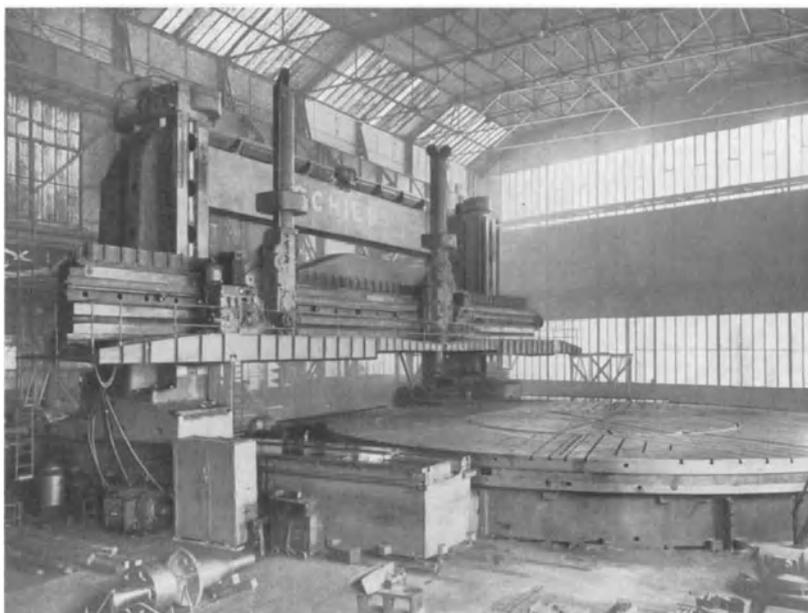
Schieß-Karusselldrehbank aus dem Jahre 1940. (Größte Werkzeugmaschine der Welt.) Größter Werkstückdurchmesser 25,5 m. Gewicht der Drehbank 1 800 000 kg.
